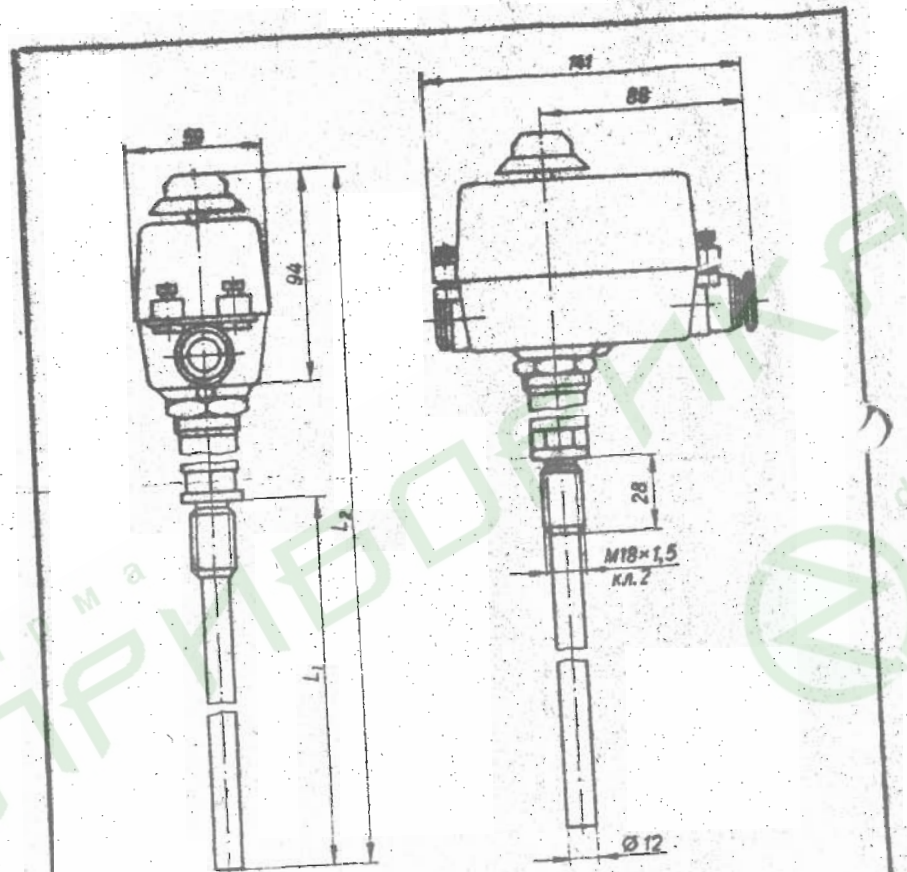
Габаритный чертеж ТУДЭ с размыкающими контактами
